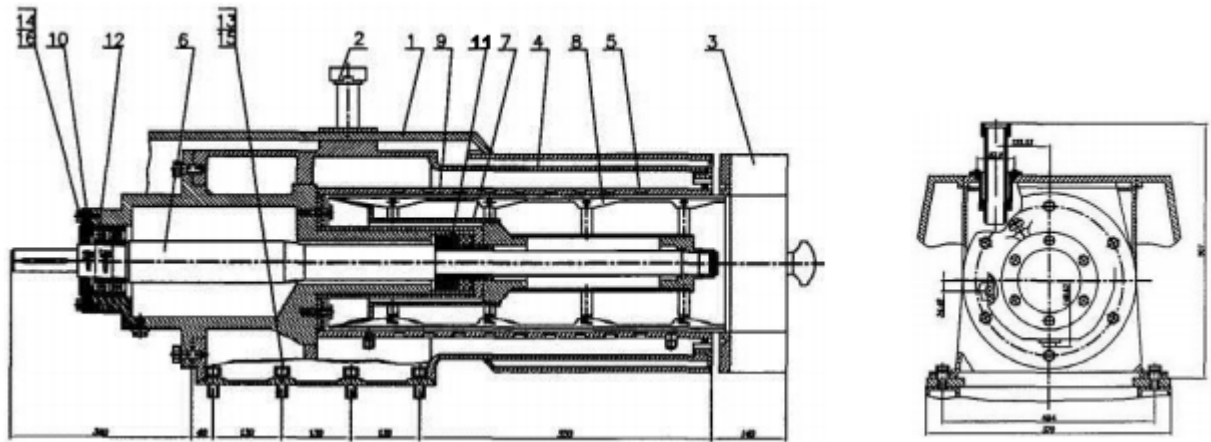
Збивач масловиготовлювача: 1 - корпус; 2 - штуцер подачі вершків; 3 - рукав; 4 - теплообмінна сорочка; 5 - сітчаста вставка; 6 - вал; 7 - корпус біла; 8 - лопата; 9 - циліндр; 10 - кришка; 11, 12 - підшипник; 13, 14, 15, 16 - болтове кріплення
